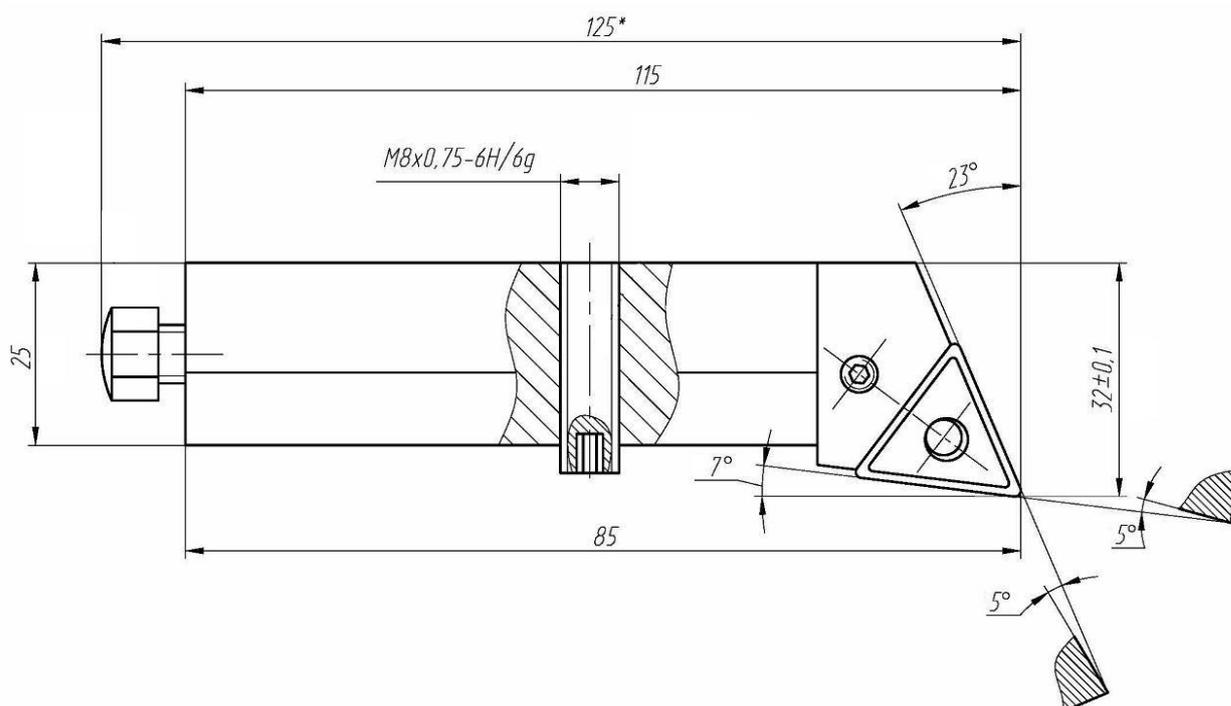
Резец токарный со сменными твердосплавными пластинами
